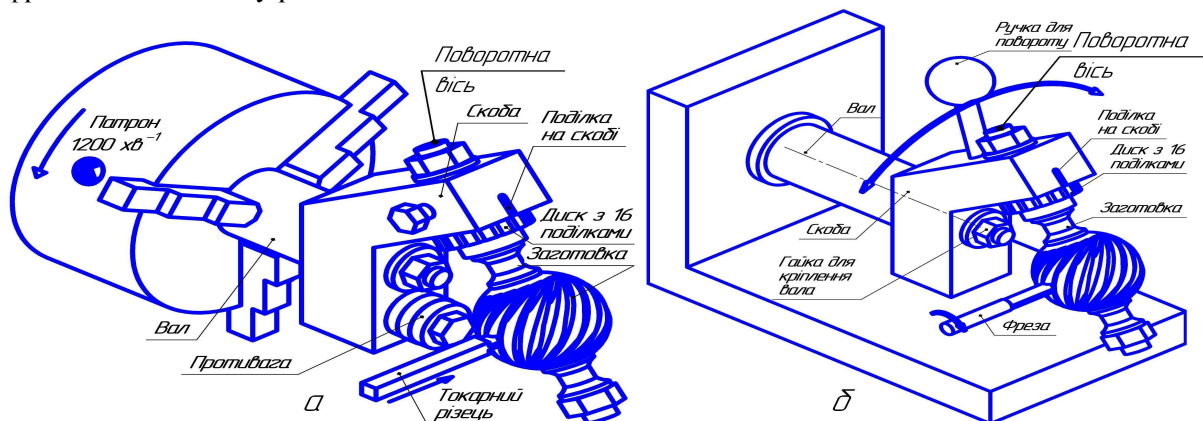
Пристрій для точіння канелюрів на сфері, який закріплюють в патроні токарного верстата (а) [1]. Принципова схема модифікованого спеціалізованого верстата для нарізання канелюрів з допомогою електрофрезера (б).
